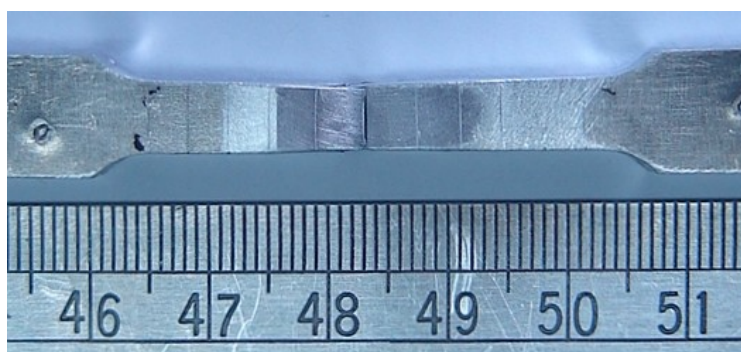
Ruptura sobre o cordão de solda FSW - geometria cônica lisa.
